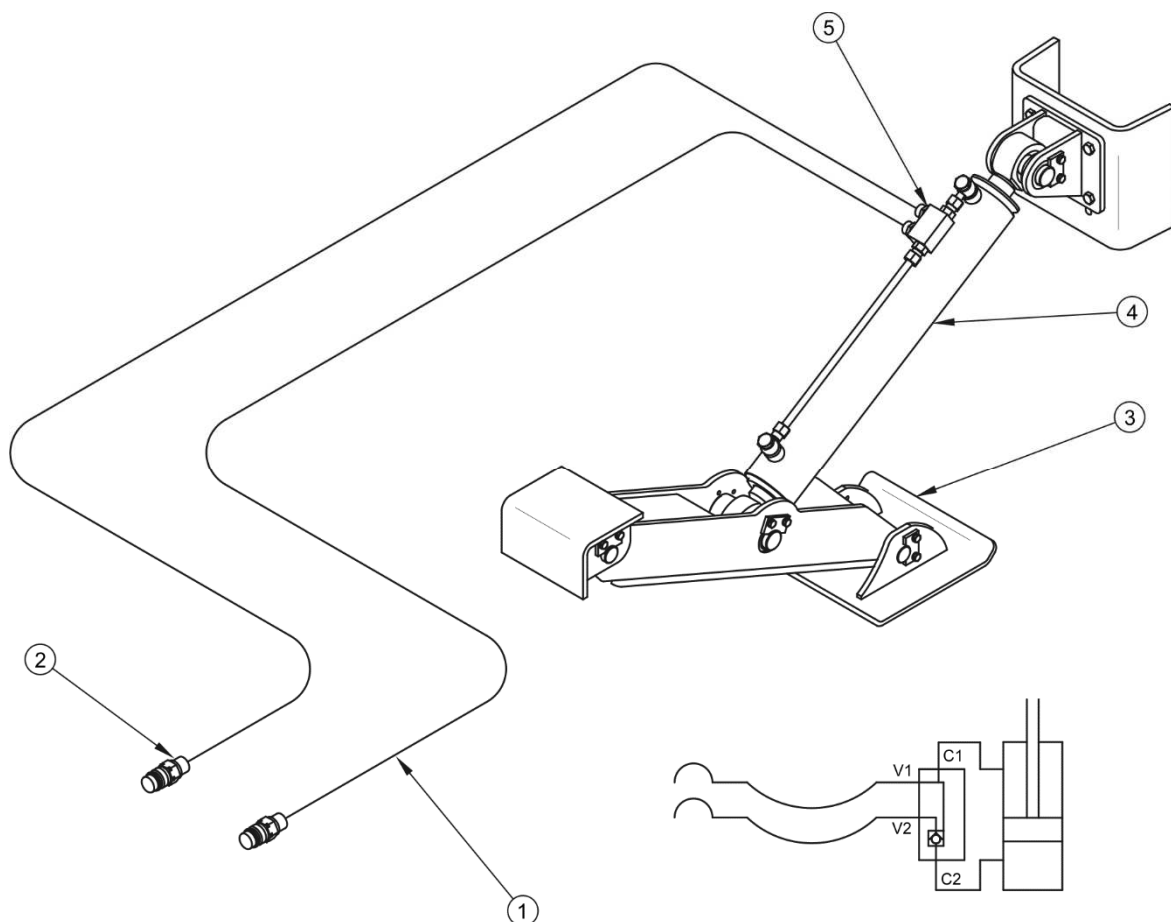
Construction et schéma de l'installation hydraulique de la béquille ciseaux
